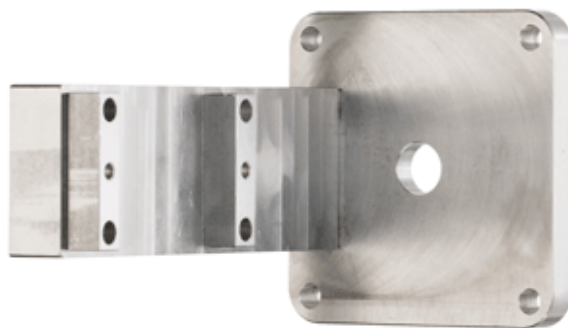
Flange MF-1040-NEMA23 [43].
